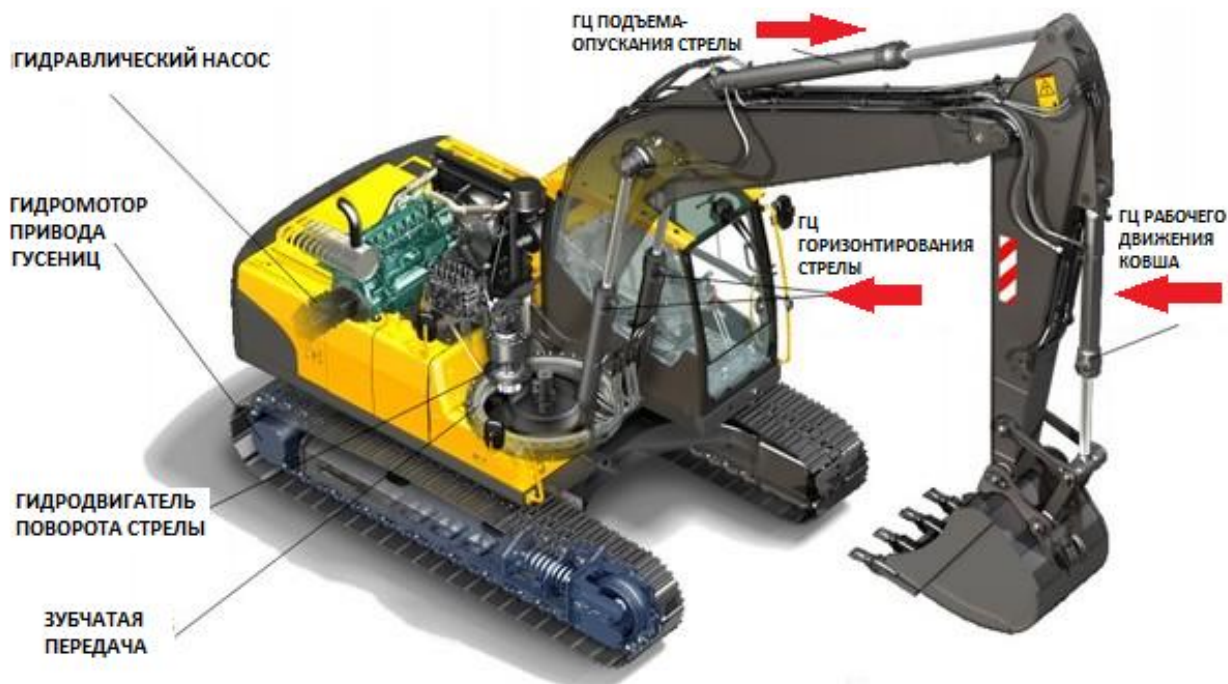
Применение силовых гидроцилиндров в приводе стрелы ковша экскаватора
